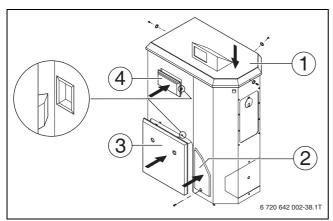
Deckel, Frontblenden und Aufbewahrungsfach montieren
